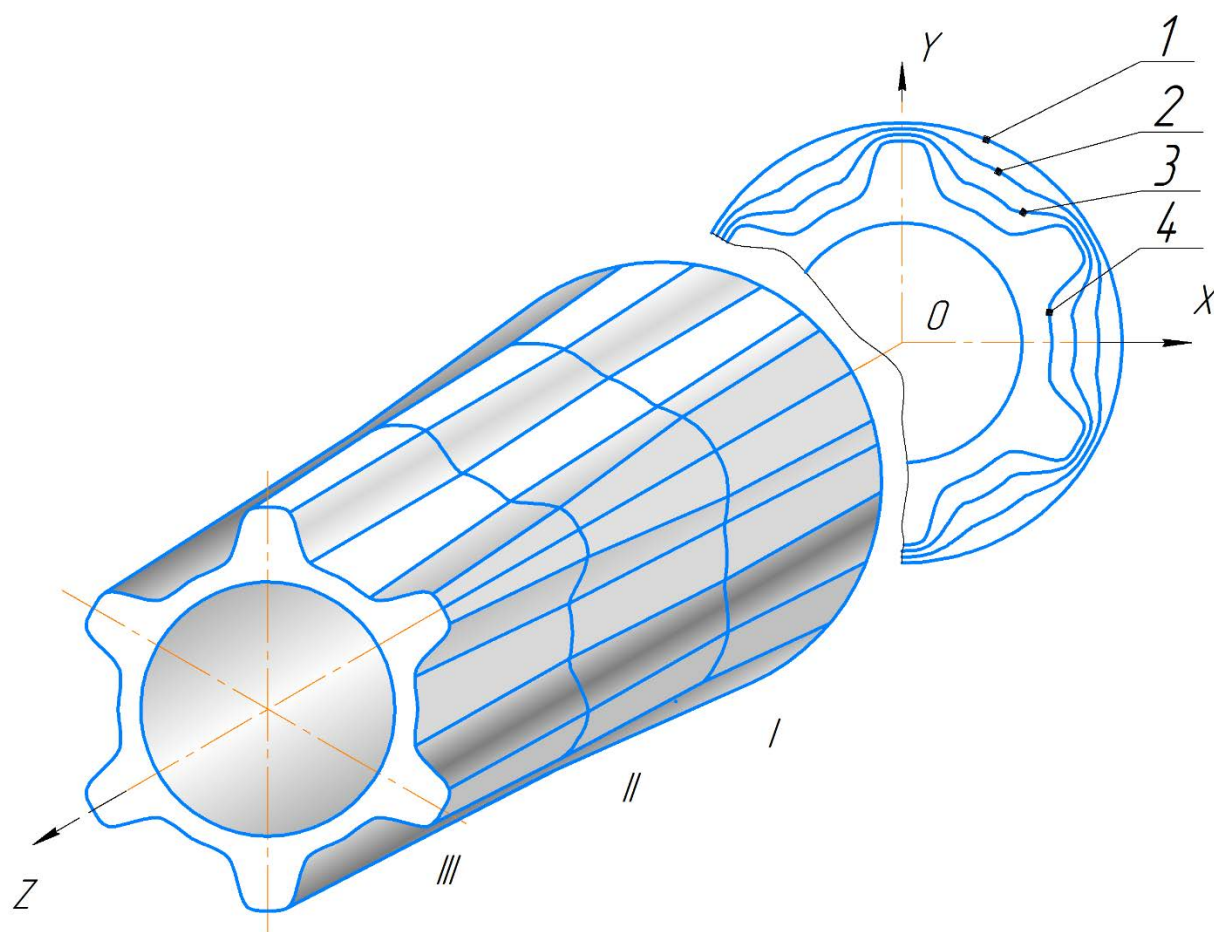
Продольный профиль инструмента при волочении криволинейного профиля в три перехода: 1 – наружный контур заготовки; 2,3 – эквипотенциали первого и второго переходов; 4 – контур готовой трубы. I, II и III – калибровка волок первого, второго и третьего переходов.
